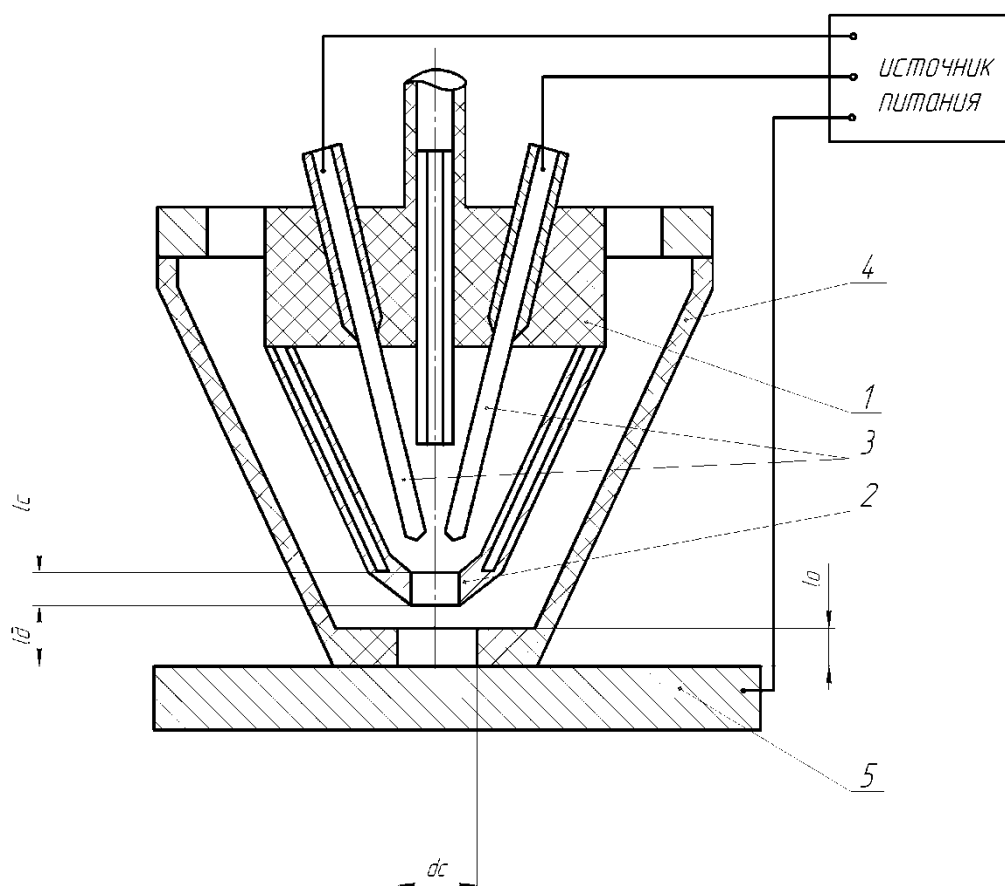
Источник питания и сварочный пистолет для точечной плазменной сварки
